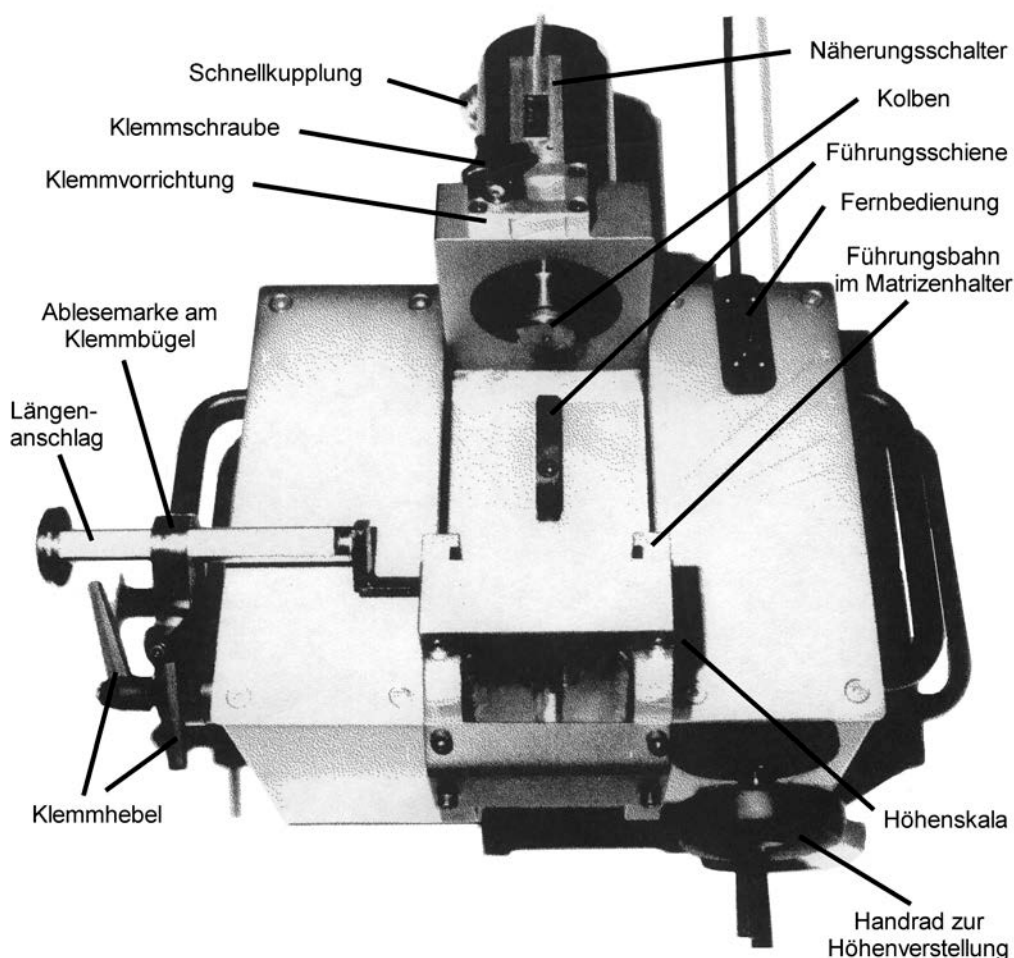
Органы управления комбинированного станка для обработки токопроводящих шин 216770
